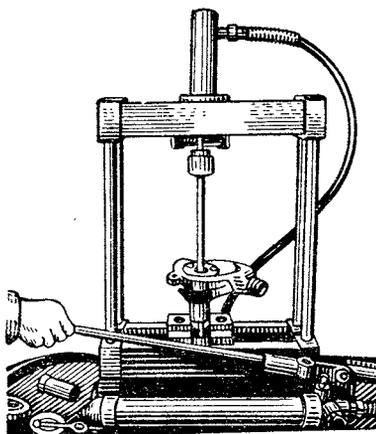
Выпрессовка валика водяного насоса с помощью гидравлического пресса ГП-20
